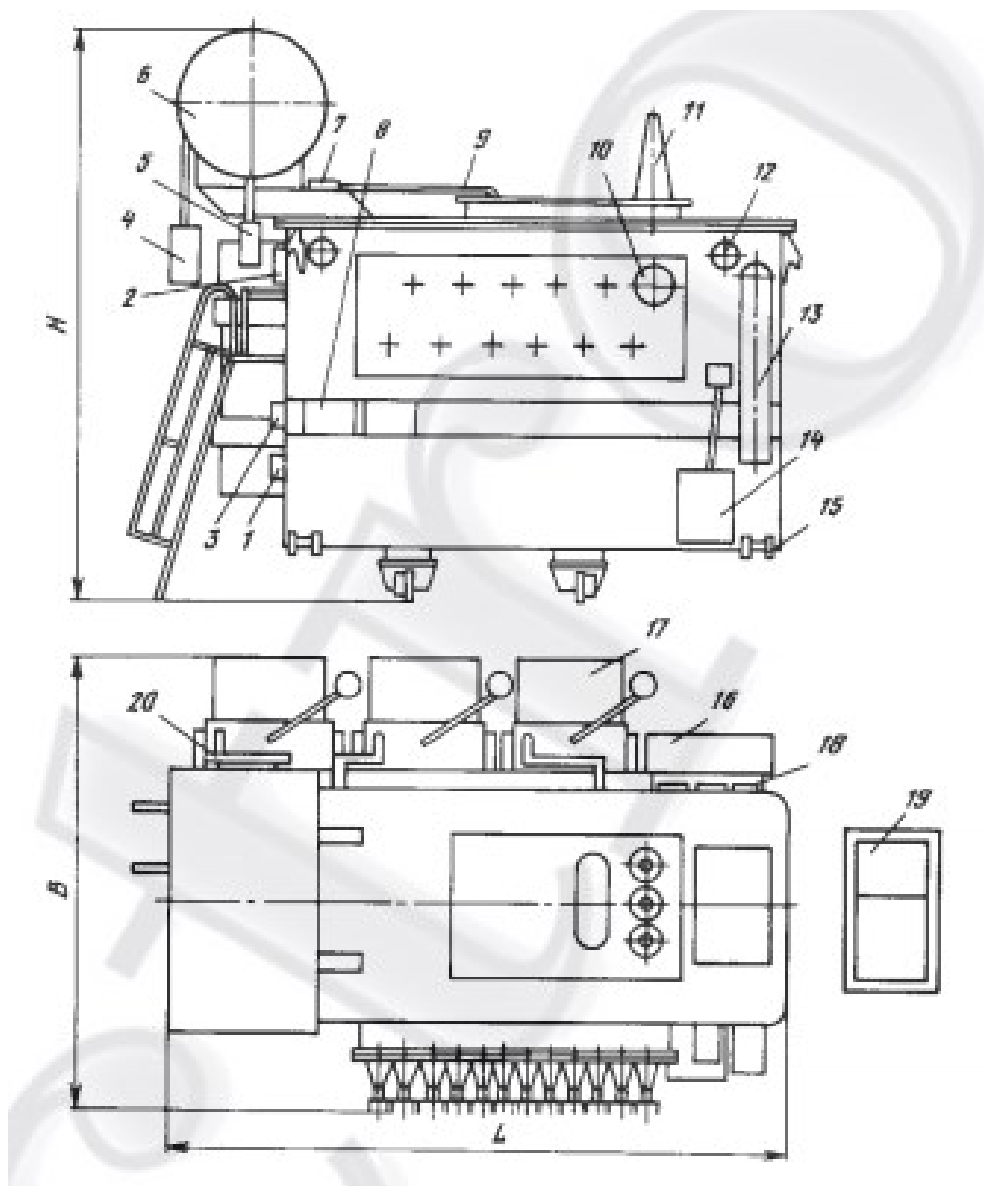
Общий вид и габаритные размеры трансформаторов ТДЦНП
